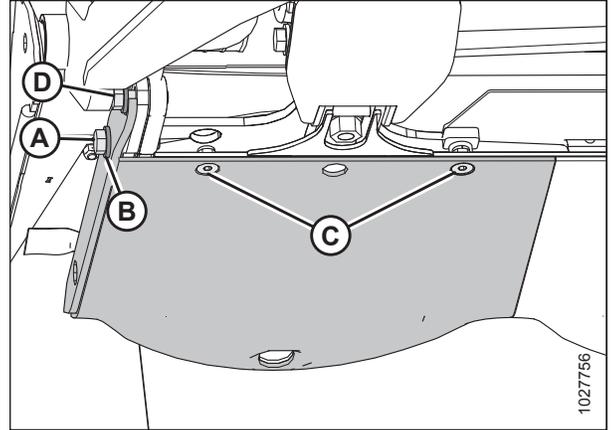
Jupe pare-pierres extérieure gauche – vue de l'arrière
